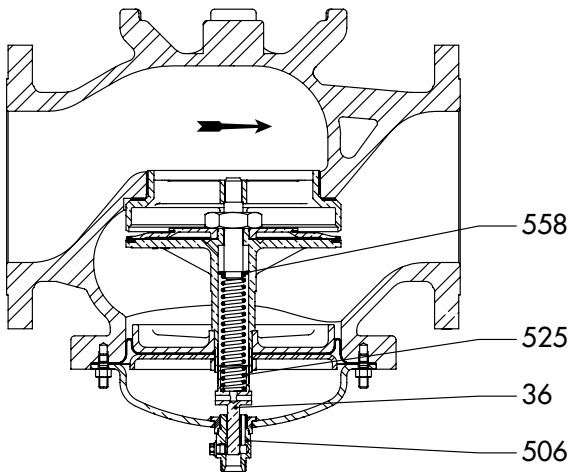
Vanne type 2422 pour DN 65 à 250 · équilibrée par membrane
